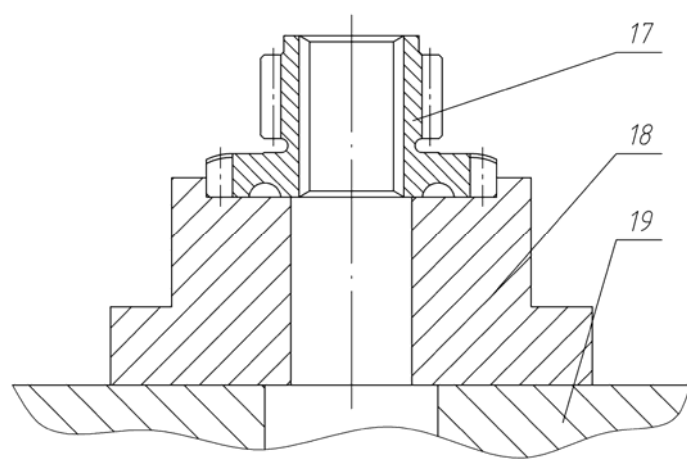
Пристрій для дорнування шліцевих отворів в корпусах деталей
